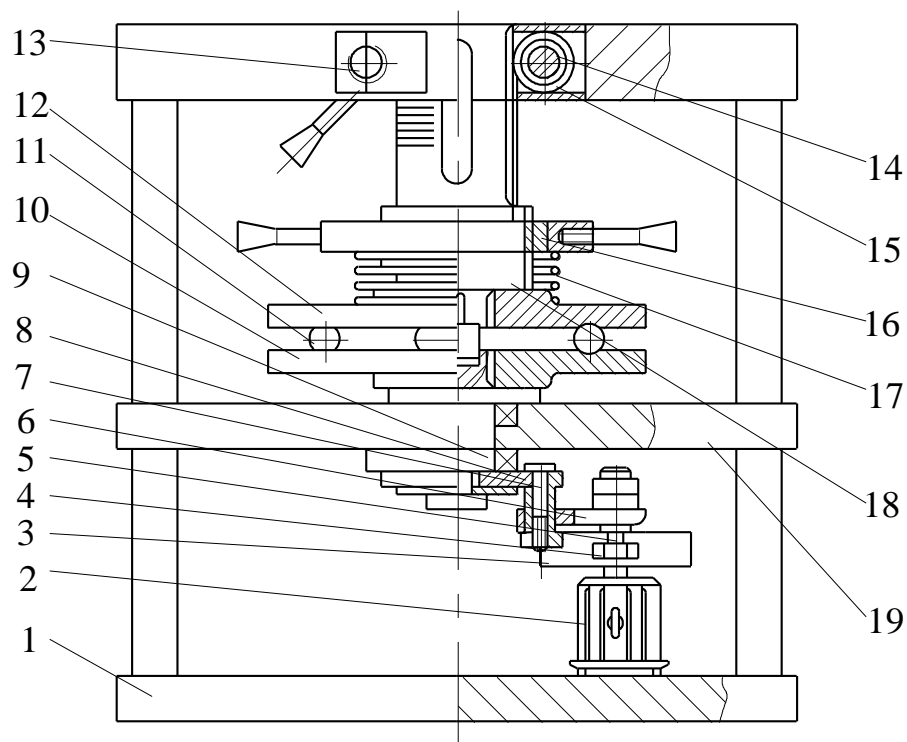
Стенд для припрацювання та тарування запобіжних муфт
